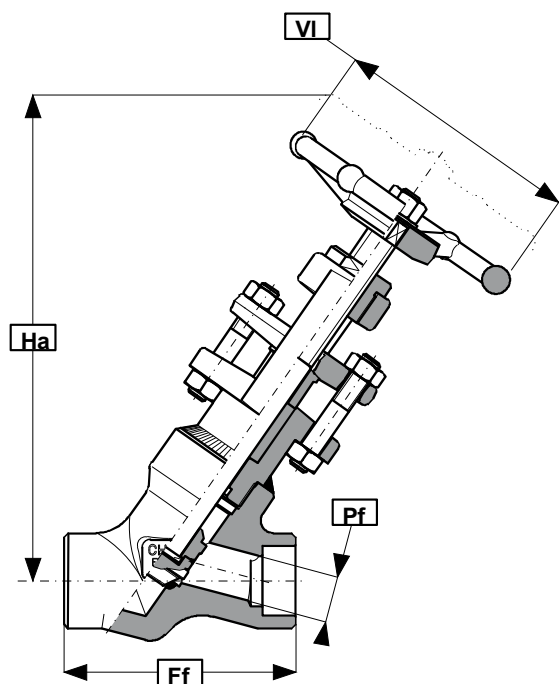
WB - GLOBO 'Y' A105/F6 TRIM N°1 - 1500LBS SW WELDED BONNET
